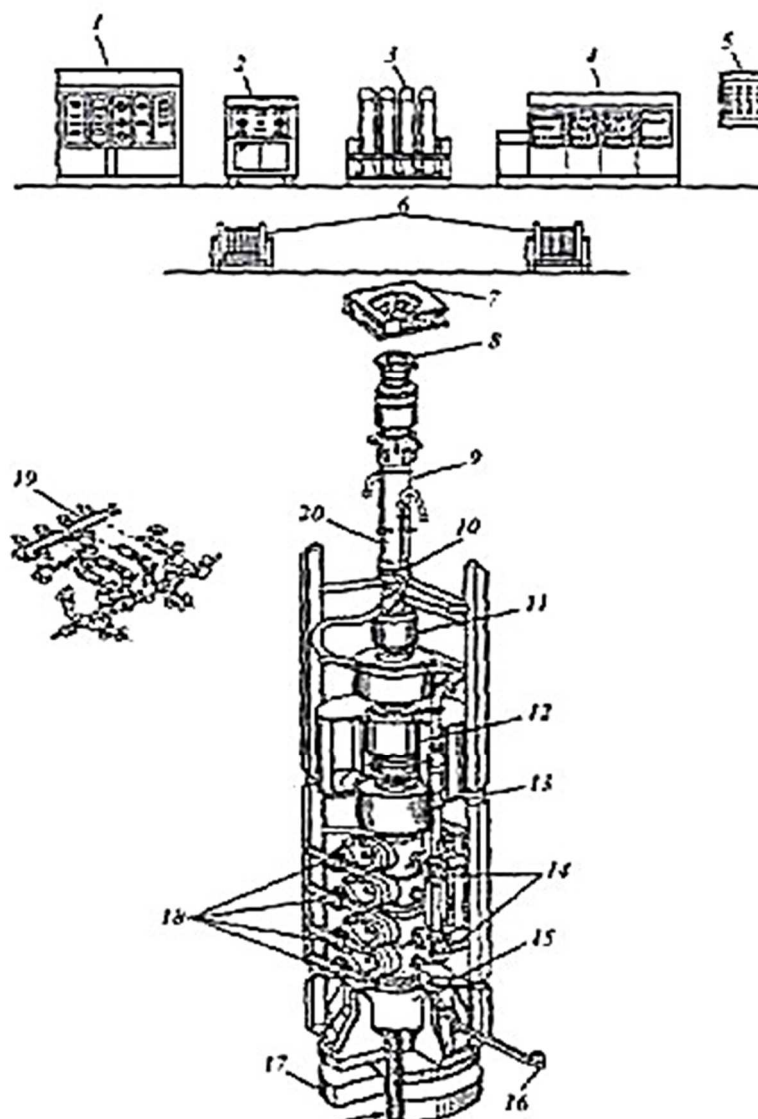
Общий вид подводного устьевоего оборудования для разведочного бурения:
